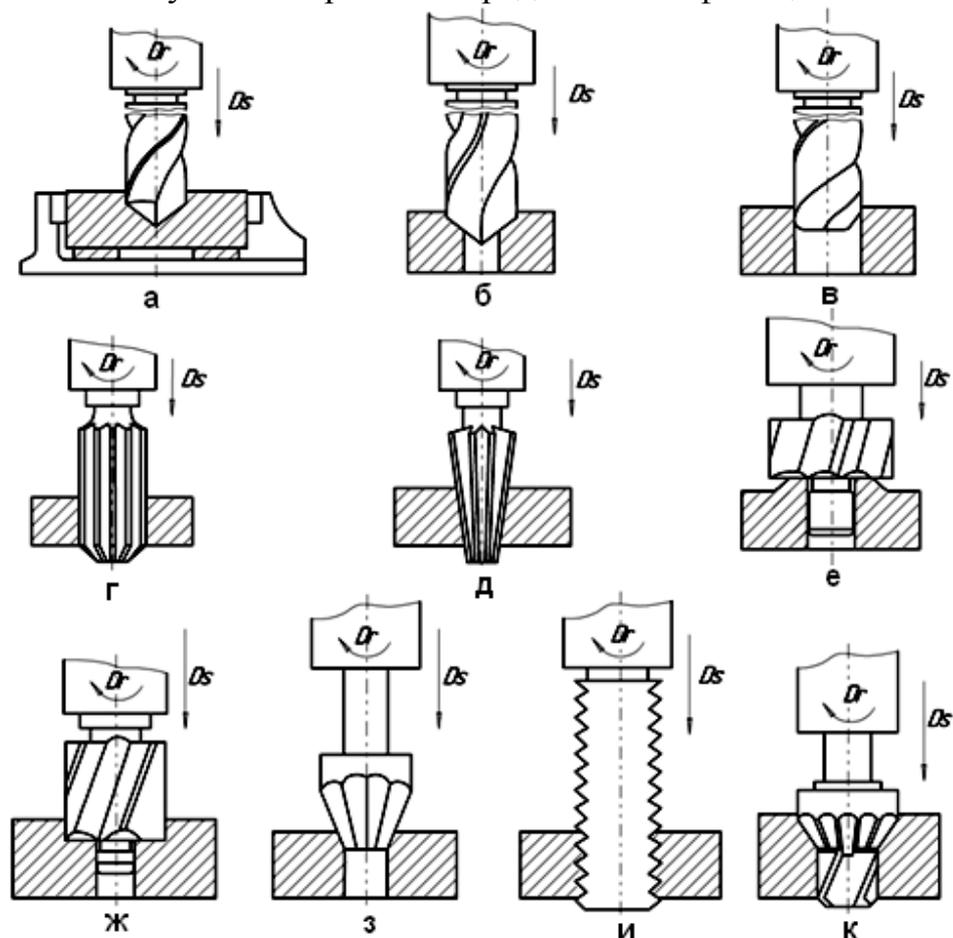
Схемы обработки отверстий на сверлильных станках.
